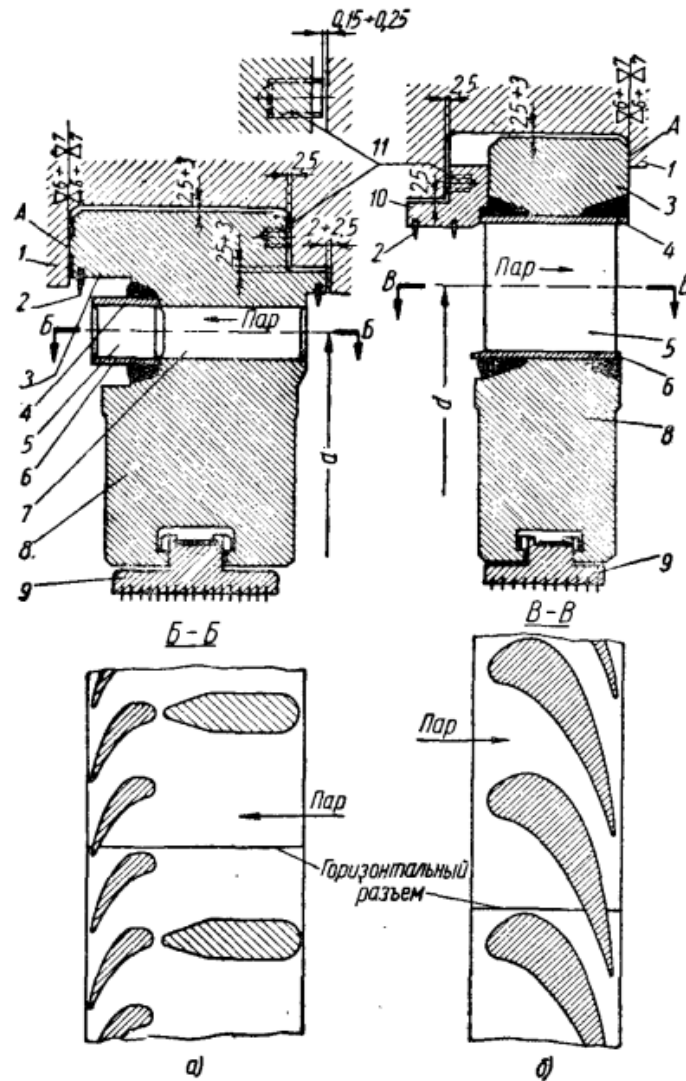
Сварные диафрагмы[1]:
